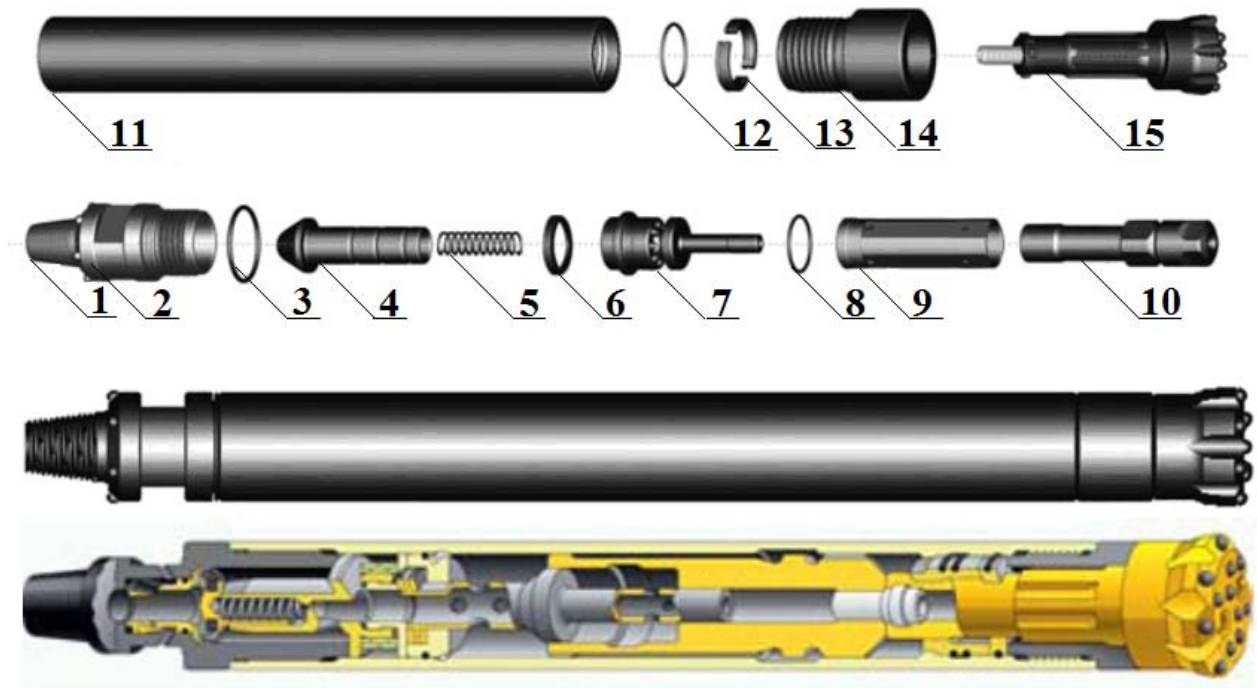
Загальний вигляд пневмоударника Atlas Copco QL-80
